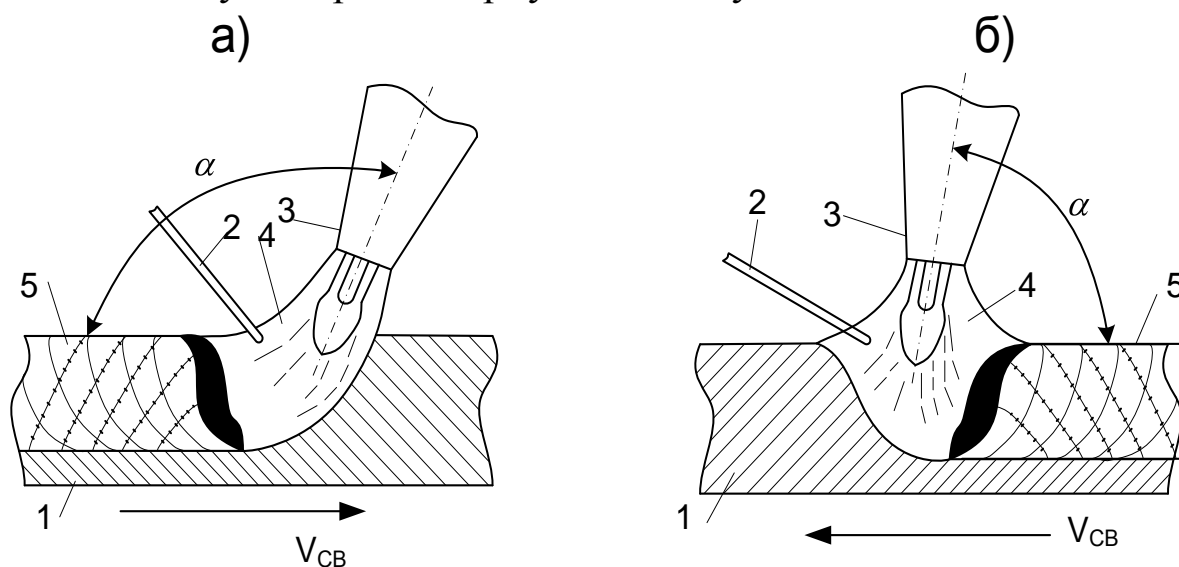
Схема газовой сварки правым (а) и левым (б) способом:
